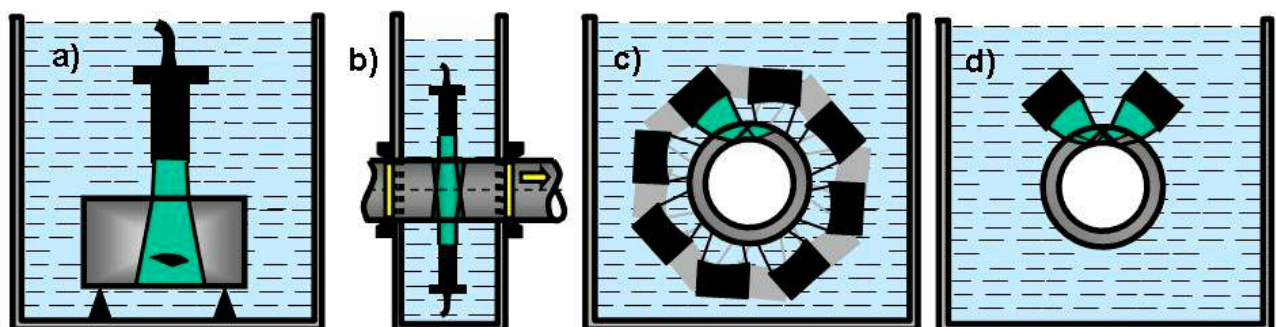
Tauchtechnik-Prüfung. a) Tauchtechnik zur Komponentenprüfung; b) HRP (Hochgeschwindigkeitsprüfung an Rund-Profilen) für Stangen und Rohre; c) HRP-Tauchtechnikprüfung von HF-geschweißten Rohren geringen Durchmessers, d) HRP-Tauchtechnikanordnung für Schweißnahtprüfung in der 12-Uhr-Position.
